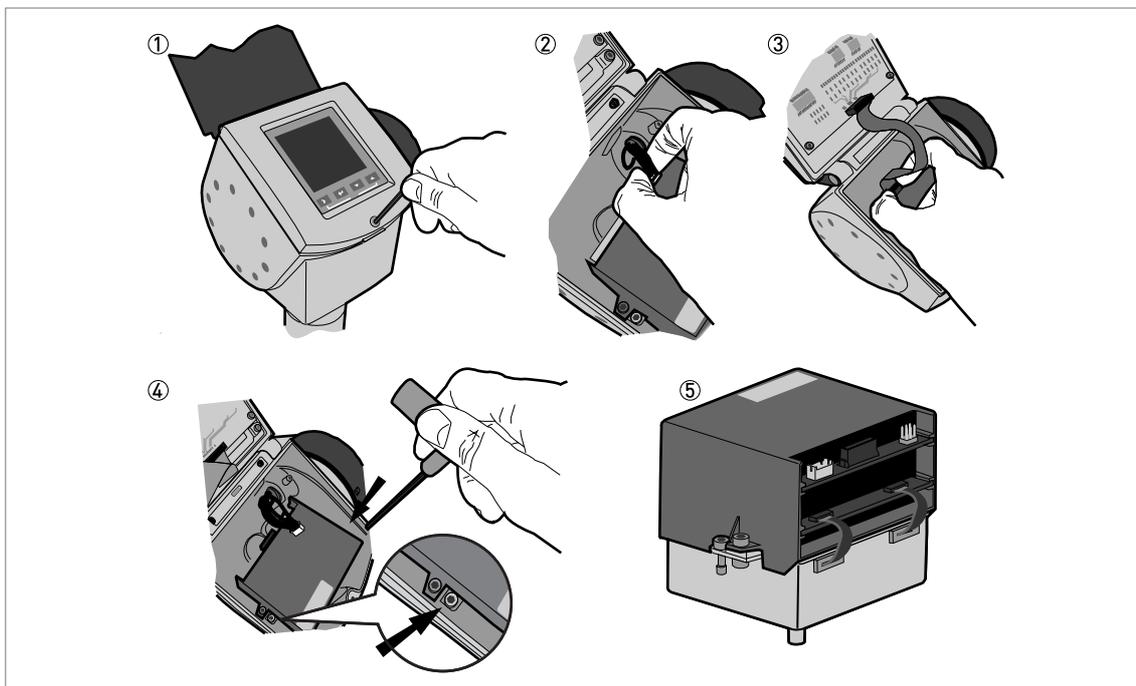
Ausbau des kompletten Elektronikmoduls.
